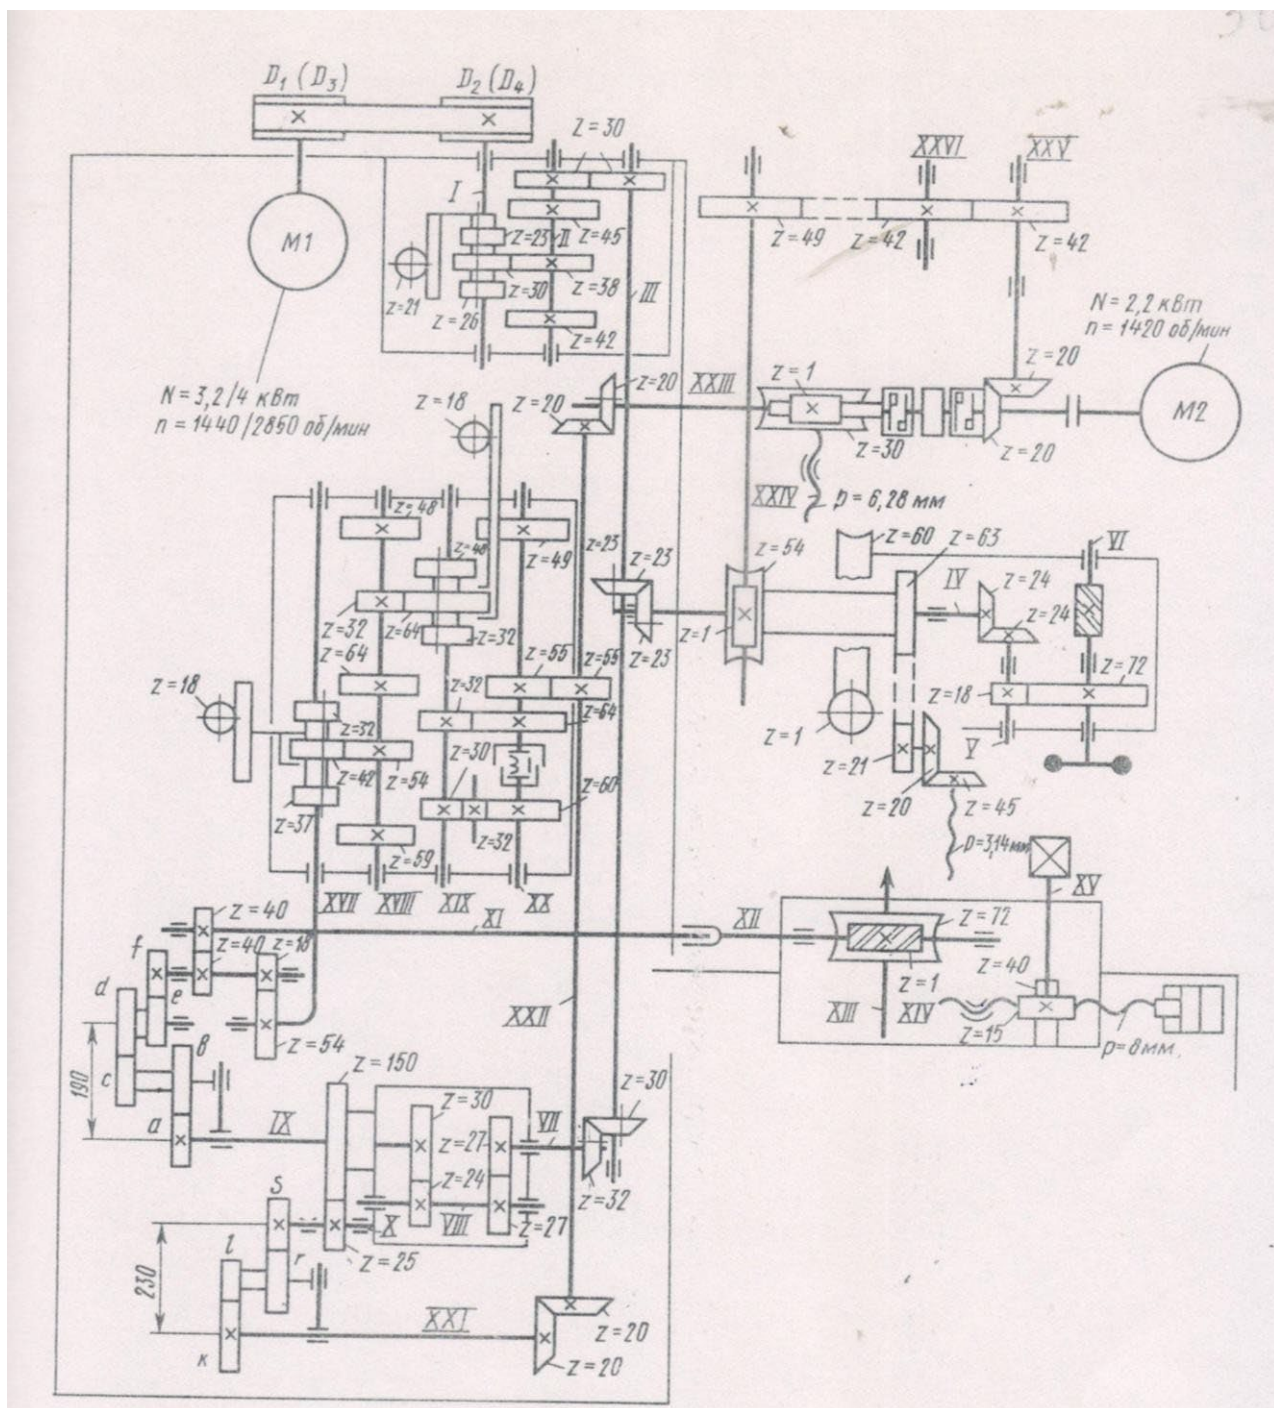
Кинематическая схема зубофрезерного станка модели 53А30
